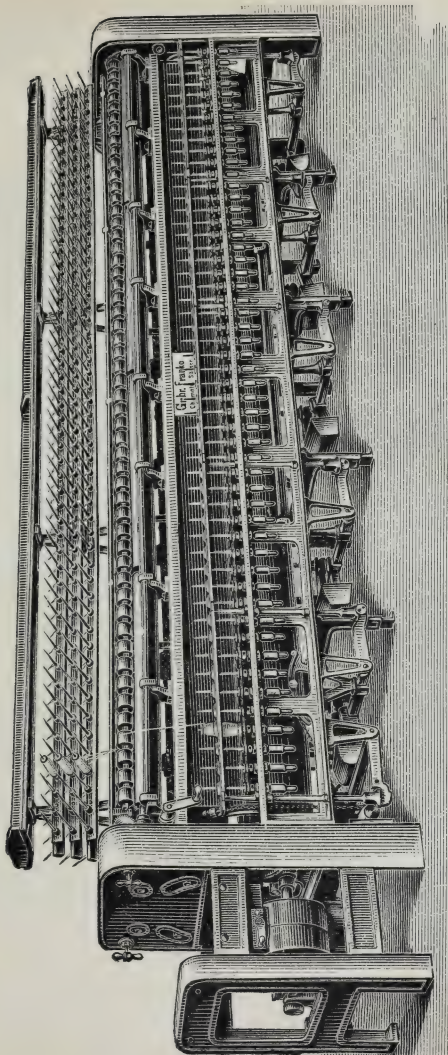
Zwirnmachine zum Rastzwirnen, von Gebr. Franke.
